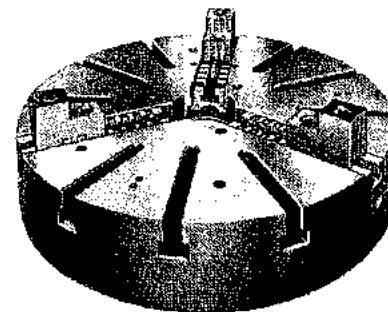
Mesa para torno revólver vertical, con tres mordazas y ranuras en T (American Steel Foundries).
